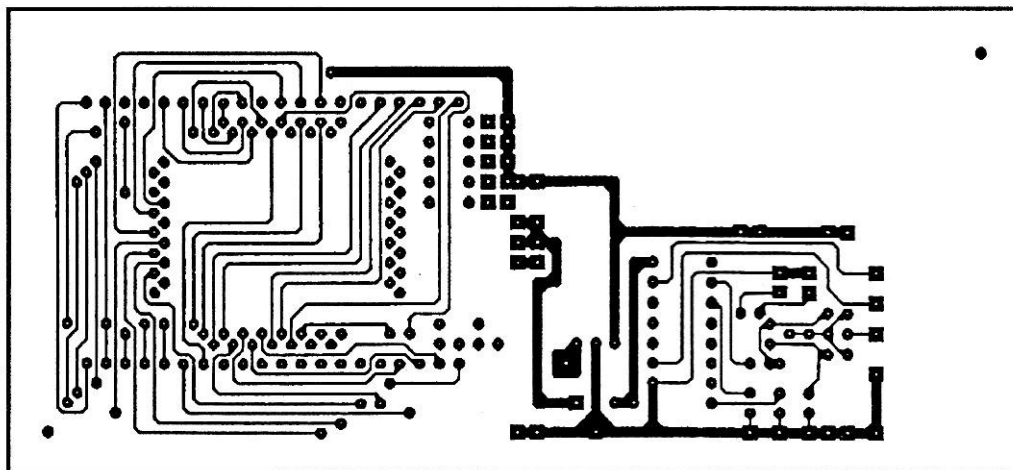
Circuit imprimé double face, trous métallisés, côté soudures.
